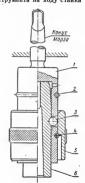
Патрон для быстрой смены режущего инструмента на сверлильном станке:
